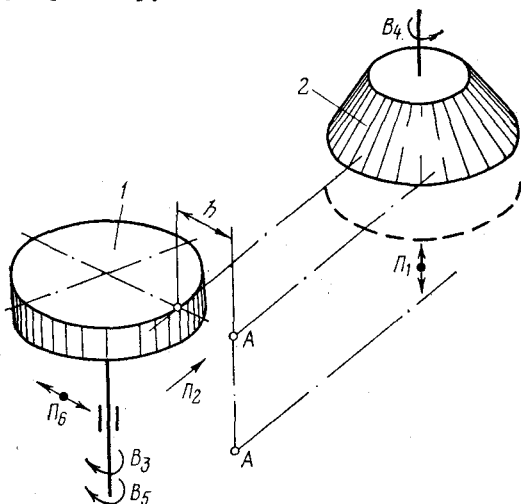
1. Способ долбления цилиндрических зубчатых колес при касательном движении врезания
